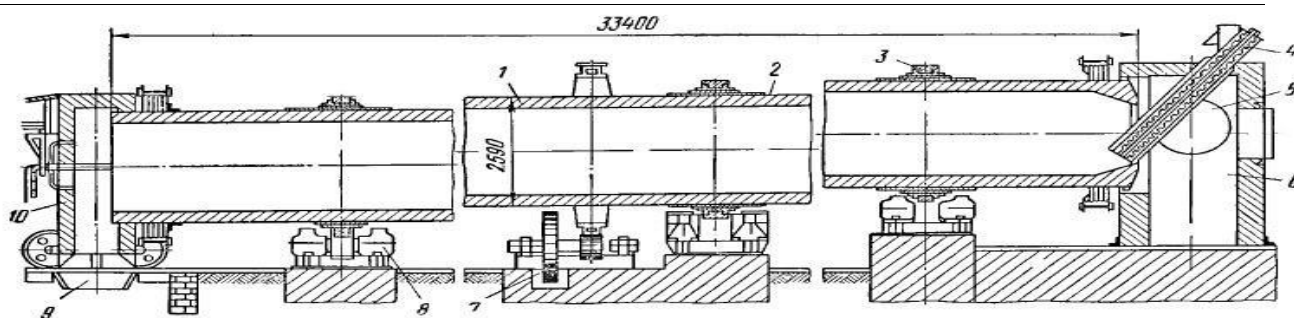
Трубчатая печь: 1- огнеупорная футеровка; 2- корпус; 3- бандаж; 4- питатель; 5- газоход; 6- пылевая камера; 7-редуктор; 8- опора; 9- воронка печи; 10- передняя часть печи
